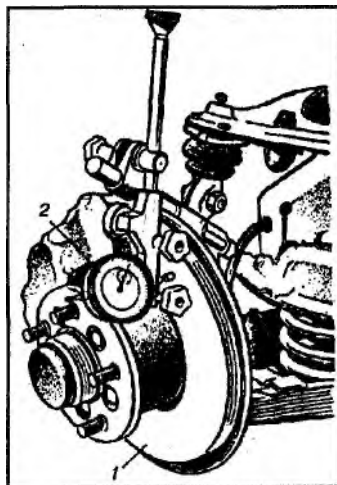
Проверка биения рабочих поверхностей тормозного диска
